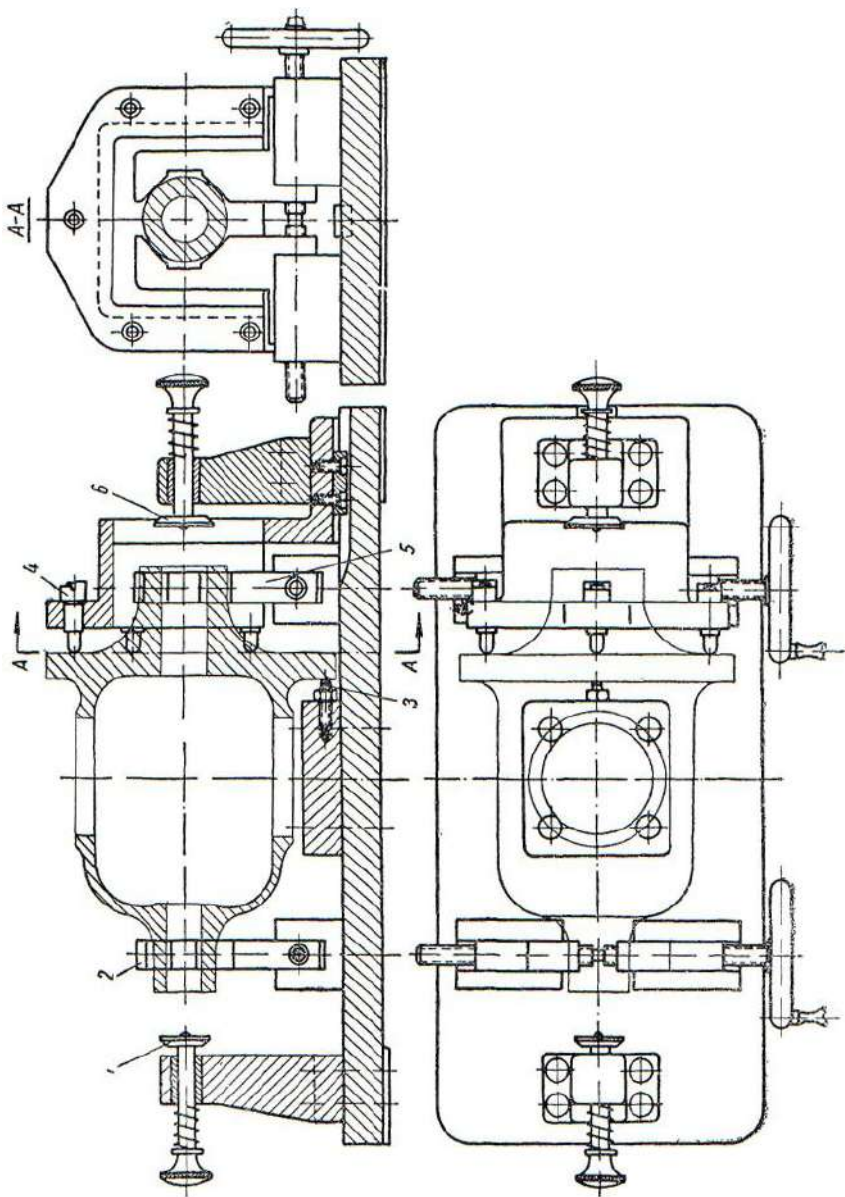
Контрольне пристосування для перевірки заготовки картера диференціала.
